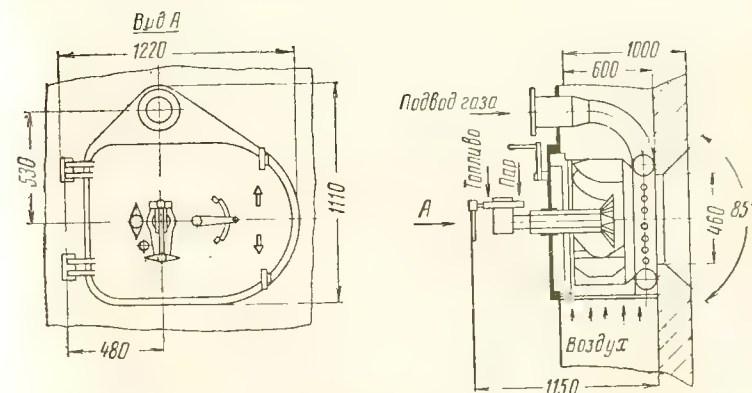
Газомазутная горелка типа ГМГБ-12.
